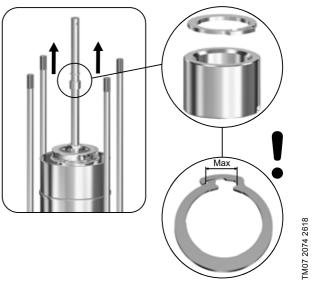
Снятие рабочего колеса (49 или 49a) с помощью приспособления Q
